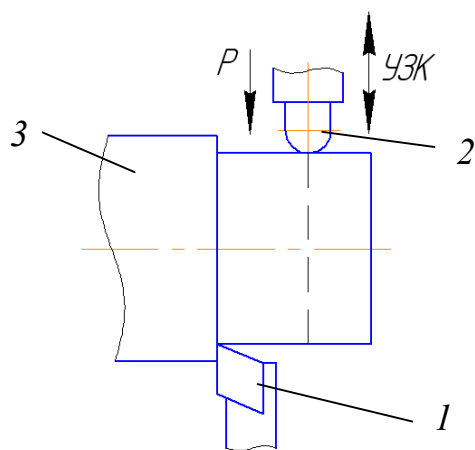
Схема комбинированной обработки точением и алмазным выглаживанием с наложением УЗК: 1 – резец; 2 – выглаживатель; 3 – заготовка
